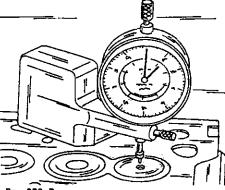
Расположение стрелочного индикатора для измерения высоты установки клапанов.
